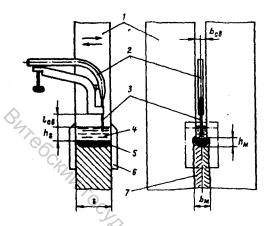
Схема электрошлаковой сварки:
